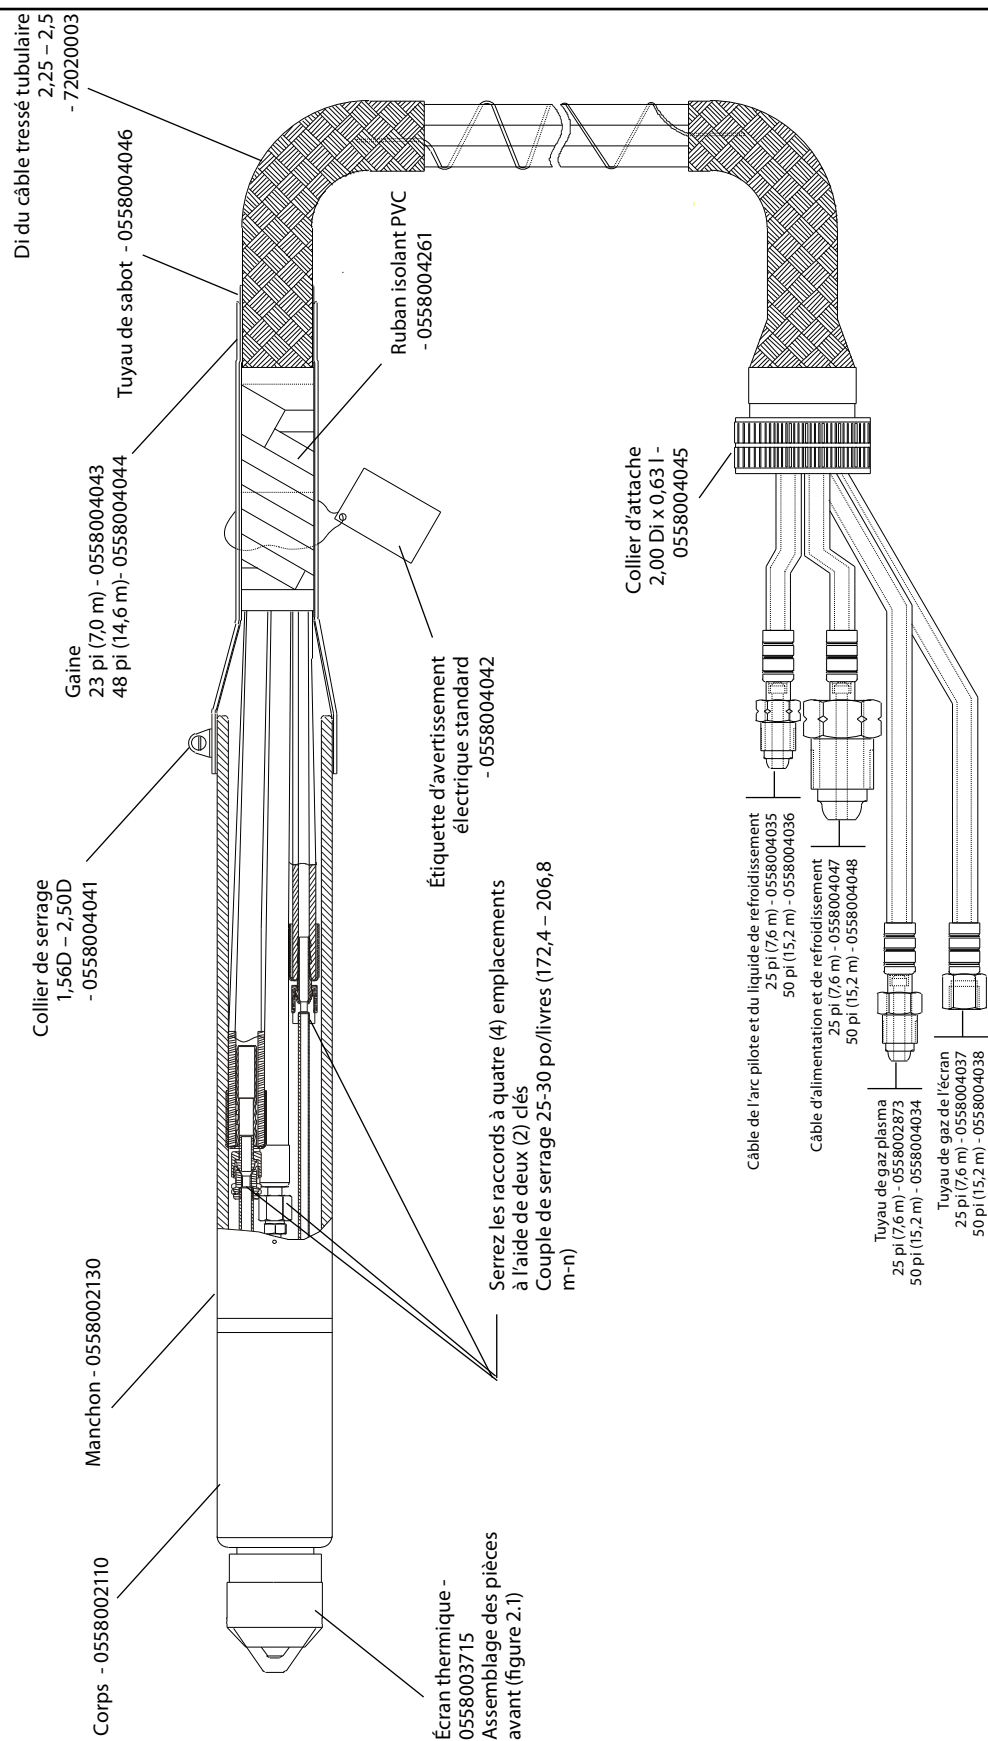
Pièces de rechange - ensemble de la torche PT-26 en ligne
